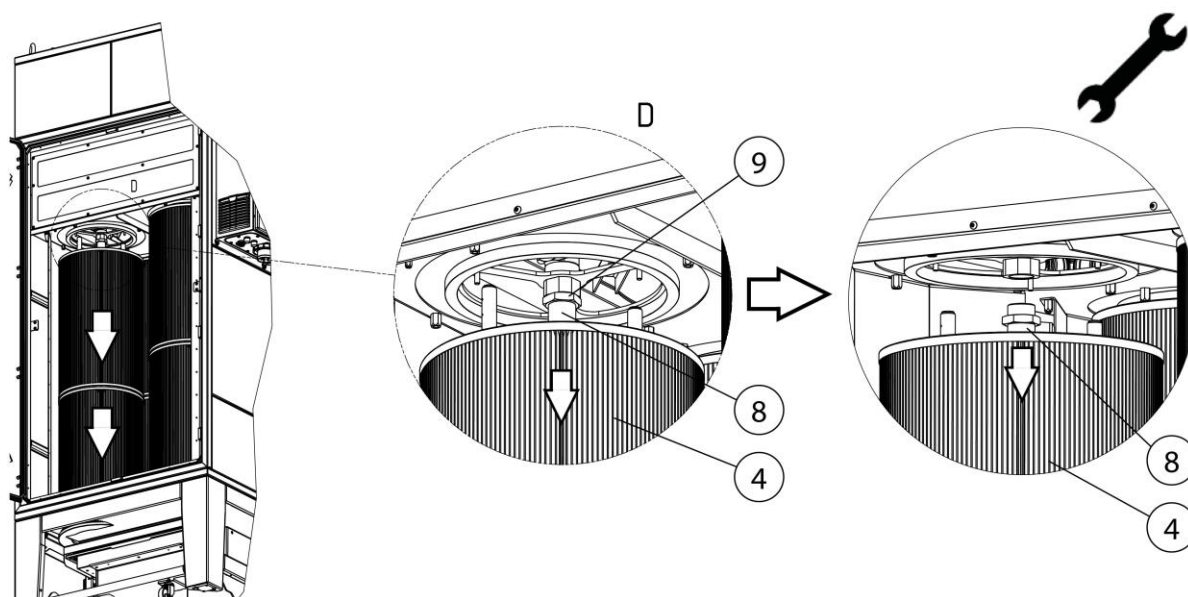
Remplacement du filtre - démontage de la buse rotative
